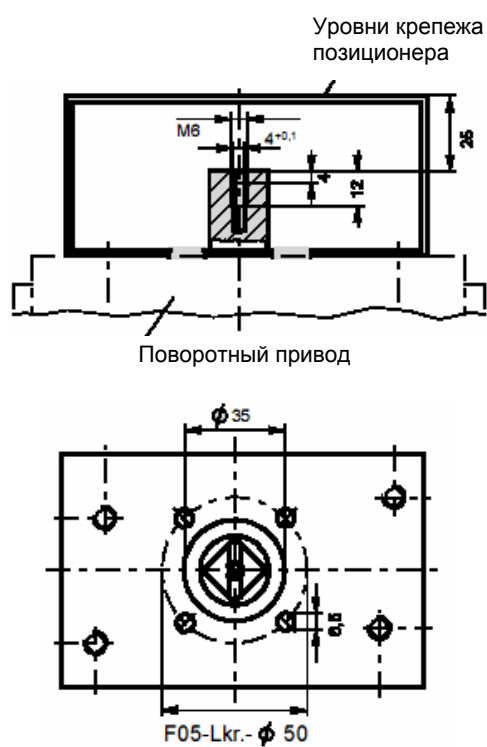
Монтаж поворотных приводов, монтажные консоли (поставляется изготовителем привода), размеры
